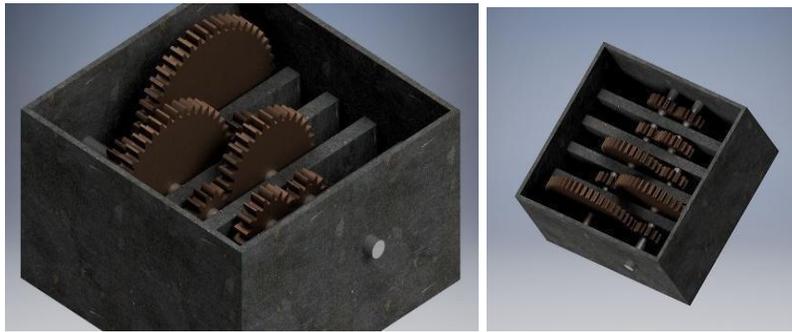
Ensamblaje de caja de transmisión prototipo 1.
